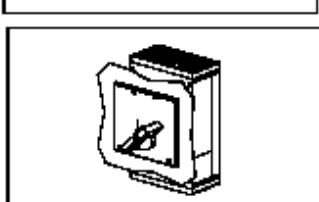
с рамкой для дверного выреза + фронтальный пов. привод
